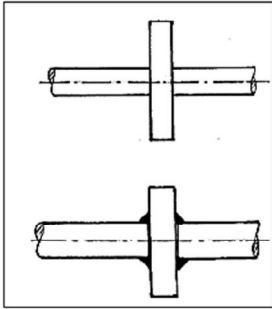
Pièce réalisée au tour et pièce soudée.
